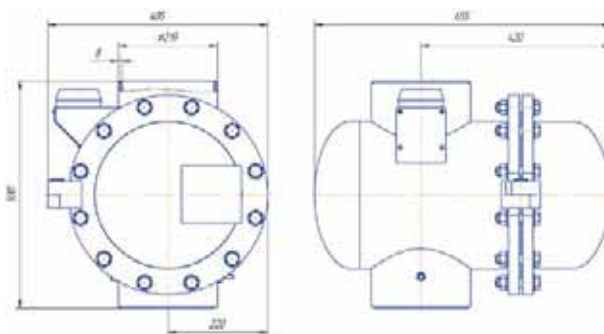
Габаритно-присоединительные размеры М21.КП-30
